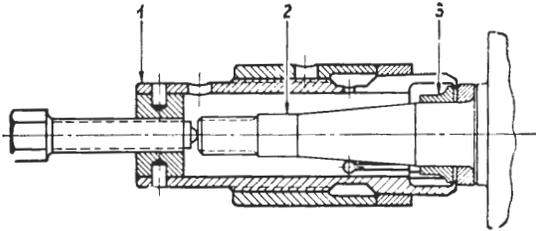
Inneren Laufring des inneren Radlagers abziehen
